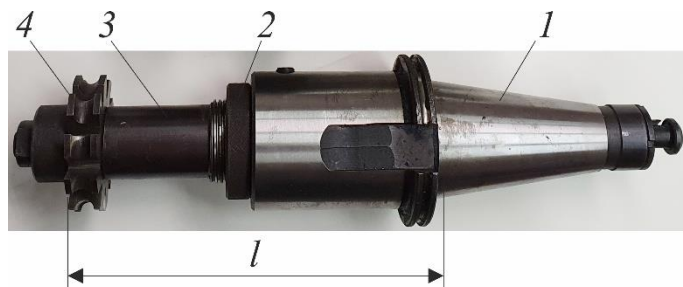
УНП для выполнения перехода фрезерования дисковой фрезой:
